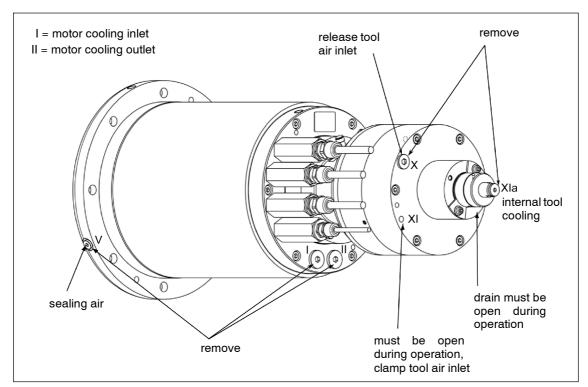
ECS-L 2SP125□ con distributore rotante
